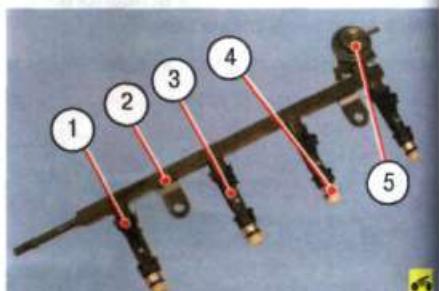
Топливная рампа: 1 – фиксатор форсунки; 2 – рампа; 3 – форсунка; 4 – уплотнительное кольцо форсунки; 5 – регулятор давления топлива
